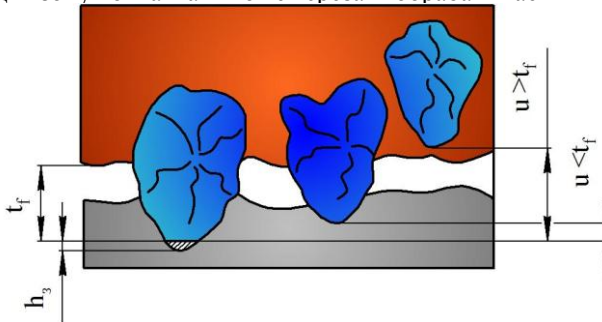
Схема зоны контакта алмазного сверла с заготовкой
